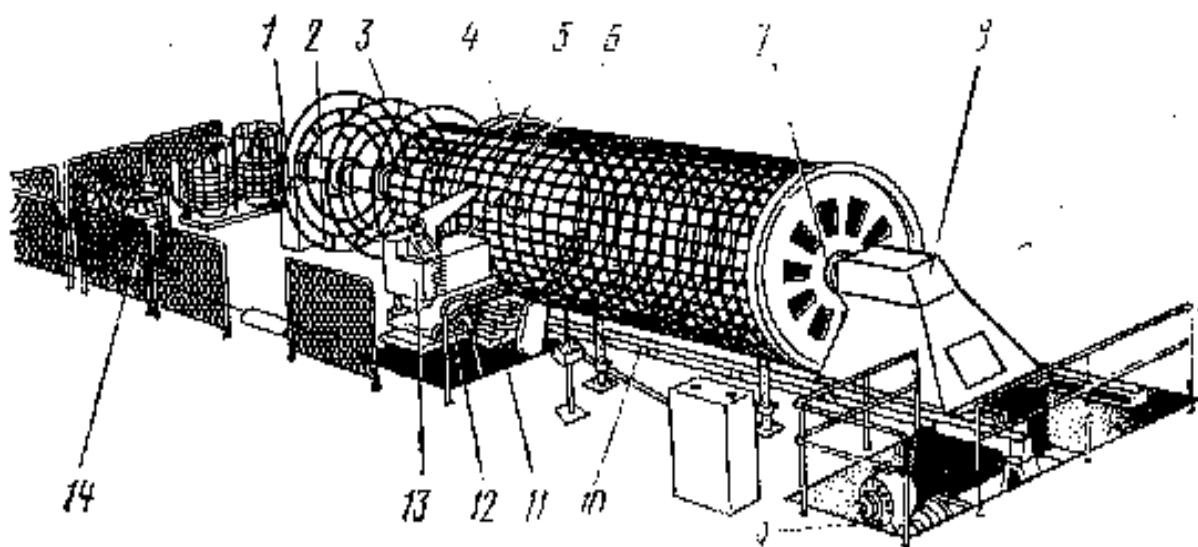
Установка СМЖ-117А для изготовления арматурных каркасов железобетонных труб
